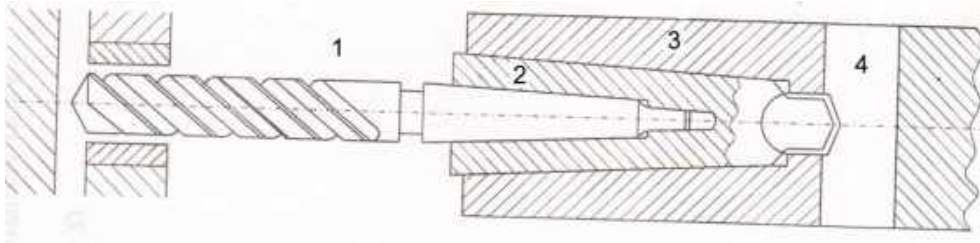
Приклад з'єднання свердла в шпинделі верстата за допомогою конуса Морзе: 1 – свердло; 2 – конус Морзе з хвостовиком; 3 – шпиндель верстата; 4 – овальний отвір у шпинделі для вибивання конуса за допомогою металевго клина, який вставляється в цей отвір
